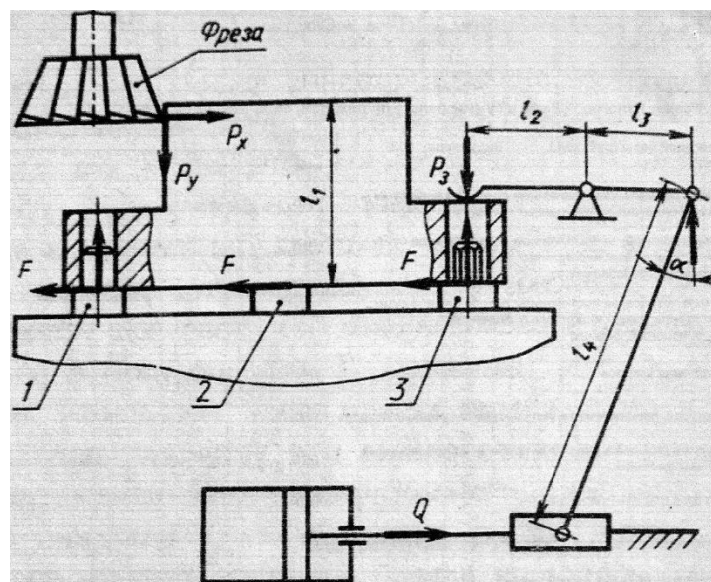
Схема сил, действующих на заготовку во время фрезерования
